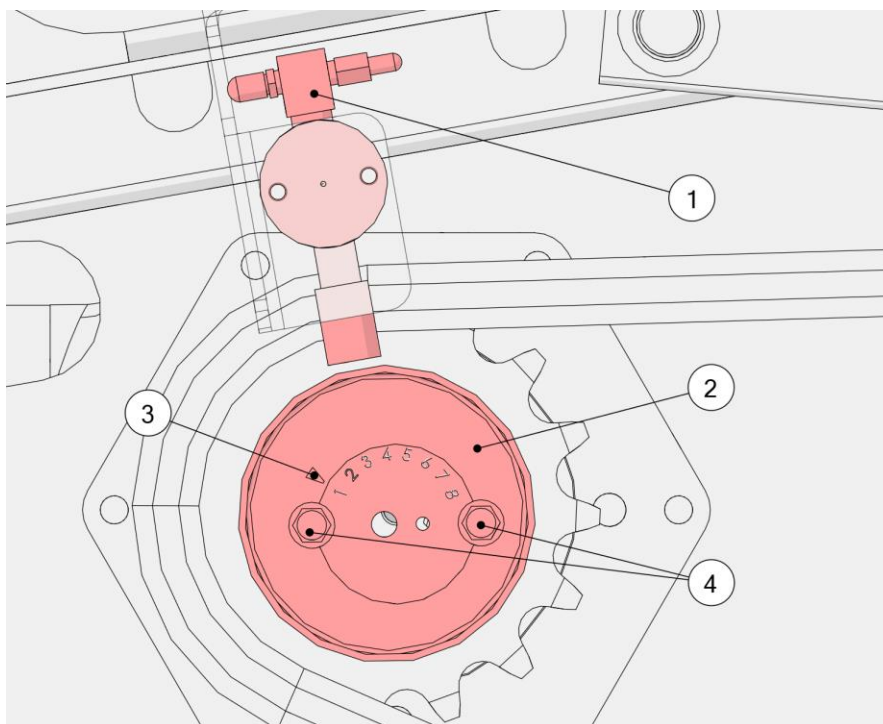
Точки смазки пресс-подборщика Z604
